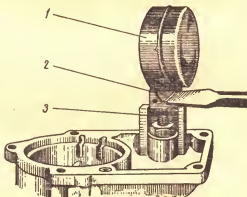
Регулировка уровня топлива в поплавковой камере подгибанием рычажка поплавка:
